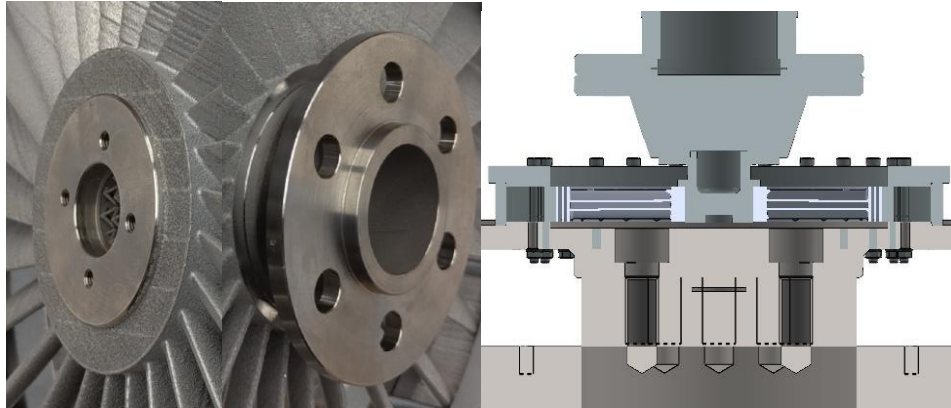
Links: Welle des Testrotors; rechts: Prüfaufbau Drehmomenttest
